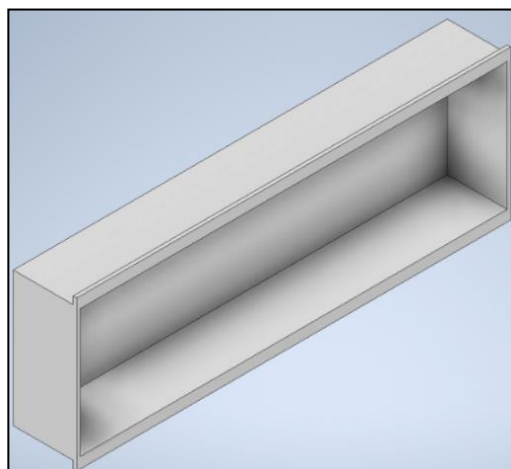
Cubiertas superiores, inferiores y laterales de la estructura metálica.
